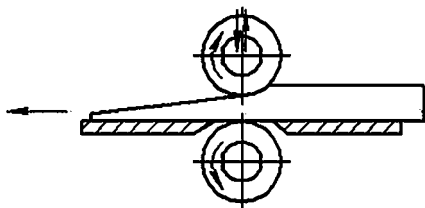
Схема прокатки в цилиндрических валках с изменением межвалкового зазора
